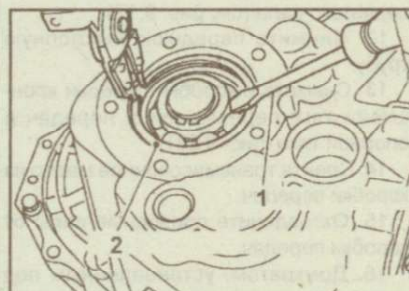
Использование пассатижей и отвертки (1) для снятия стопорного кольца (2) крепления подшипника вторичного вала
